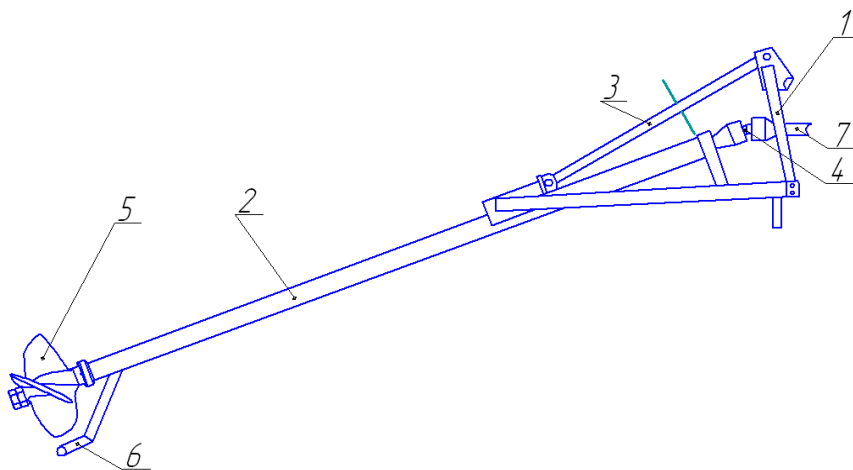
Общий вид гомогенизатора навесного: 1 – навеска; 2 – рама; 3 – талреп; 4 – вал; 5 – винт; 6 – упор; 7 – карданный вал
